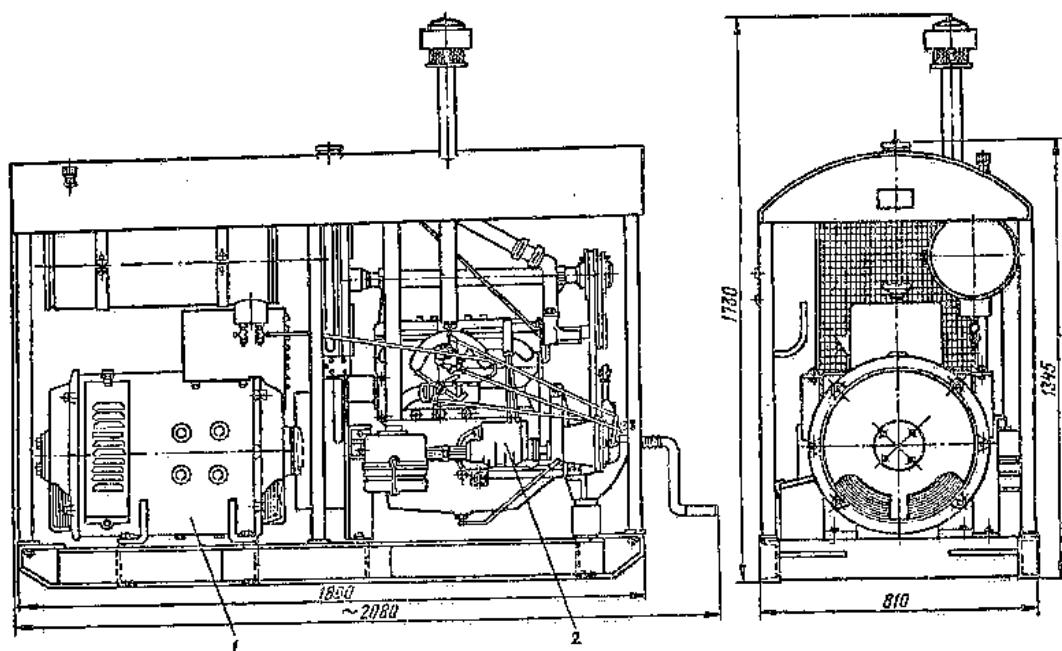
Схема конструктивного исполнения сварочного агрегата АСБ-300:
